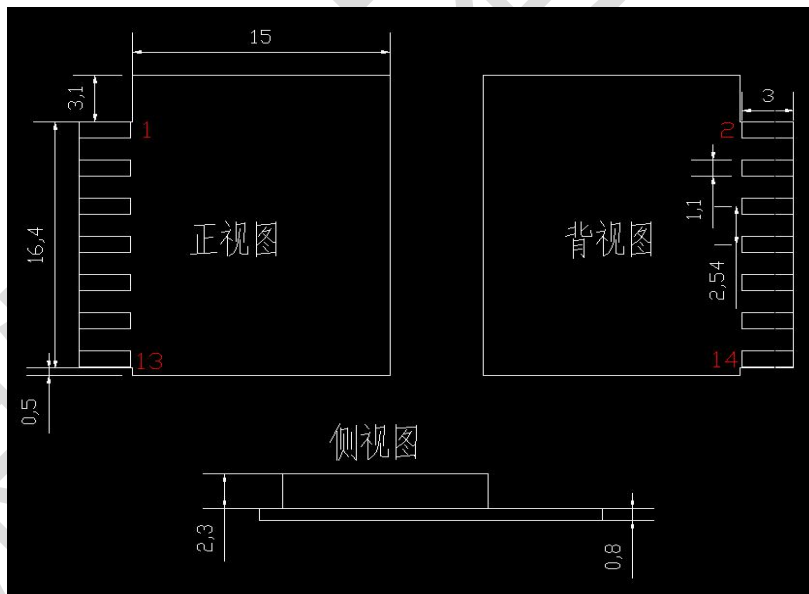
FST66_14A 模组尺寸平面图 (单位: mm)
